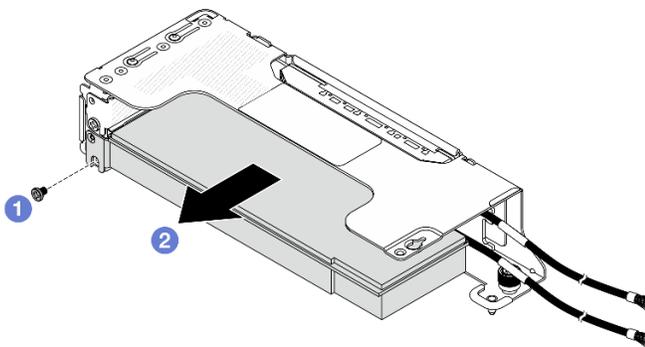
Remoção de um adaptador PCIe da gaiola da placa riser 2LP
